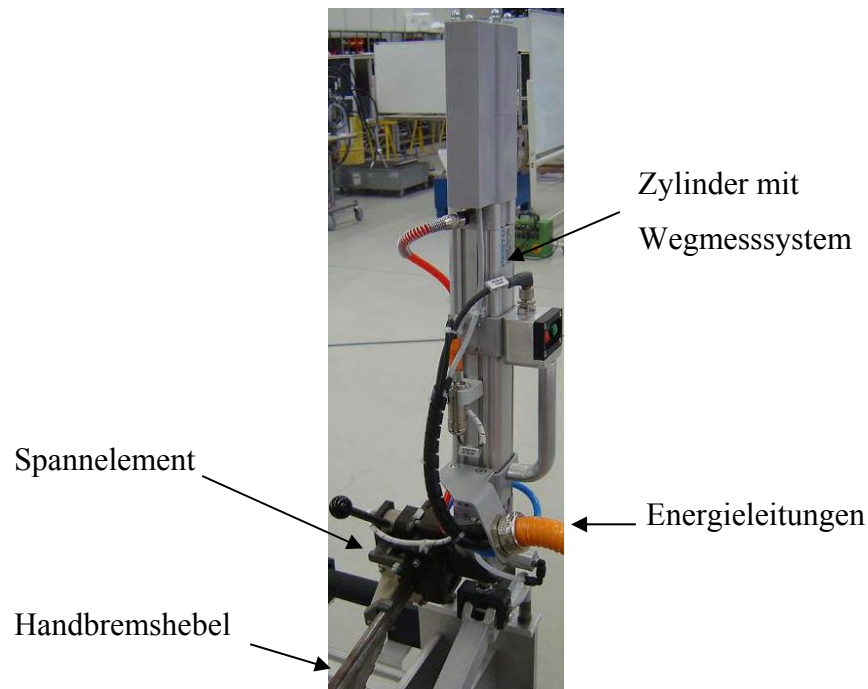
pneumatisches Einstellwerkzeug ¹²
